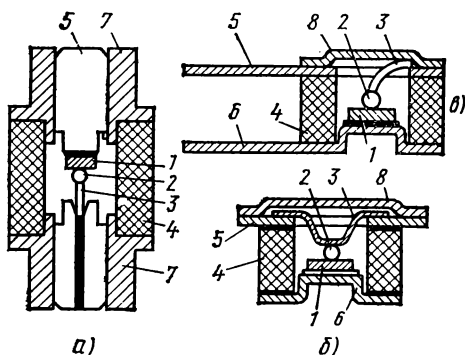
Конструкции туннельных диодов: а — патронного типа; б — таблеточного типа; 5 — с ленточными выводами; 1 — корпус; 2 — электродный сплав, формирующий *p-n*-переход; 3, 8 — выводы; 4, 7 — втулки корпуса; 5 — полупроводниковый кристалл; 6 — соединительный электрод; 9 — крышка
